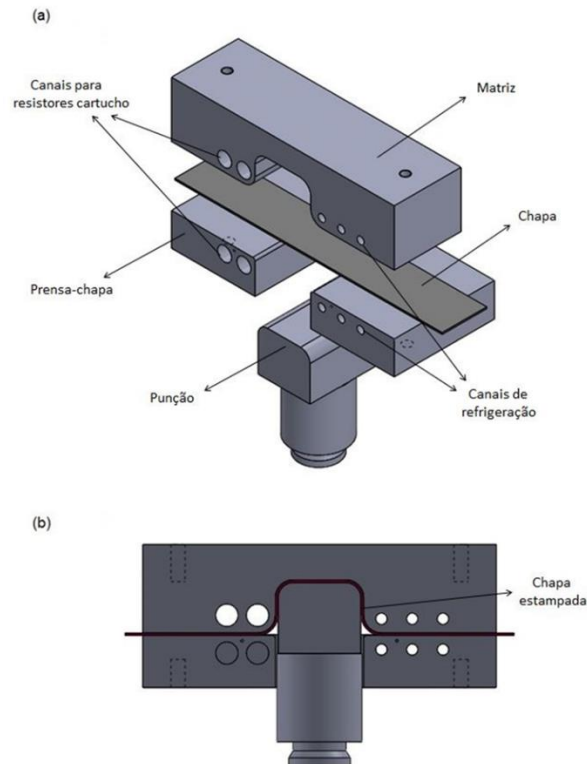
a) Vista isométrica do ferramental e do corpo-de-prova antes da conformação e b) Vista frontal do ferramental após a estampagem.
